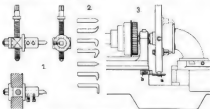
Stahlhalter für Planscheiben von Leitspindel-Drehbänken.
